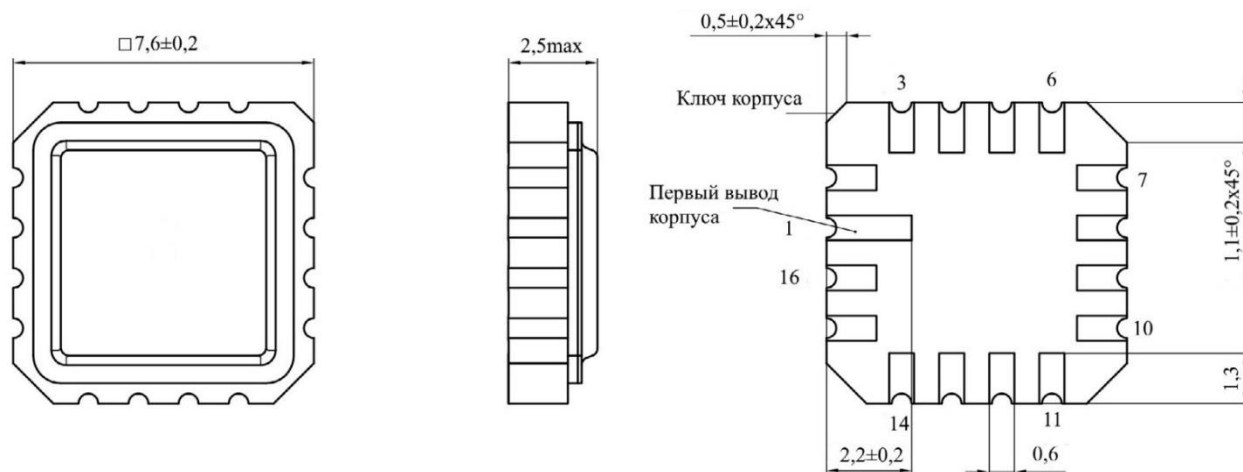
Габаритный чертеж корпуса МК 5119.16-А (размеры в мм)
